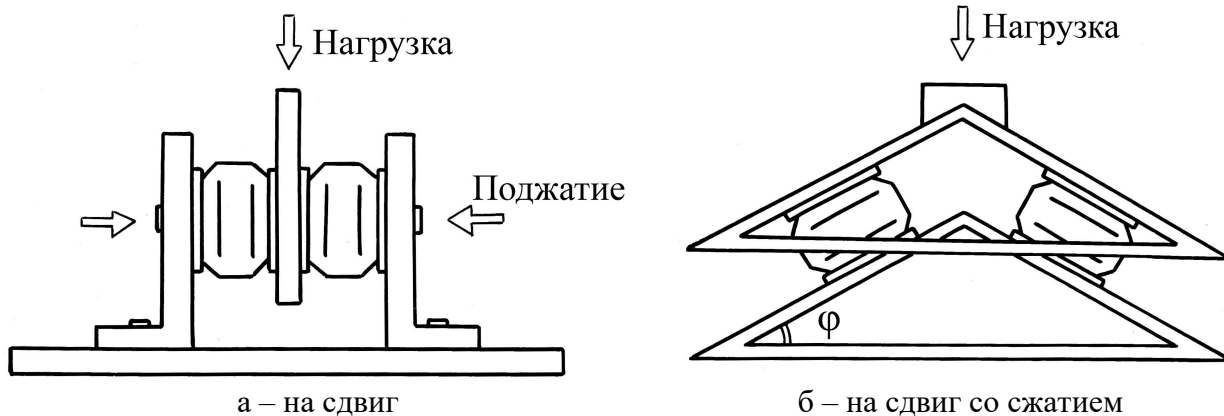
Приспособления и схемы нагружения виброизоляторов
